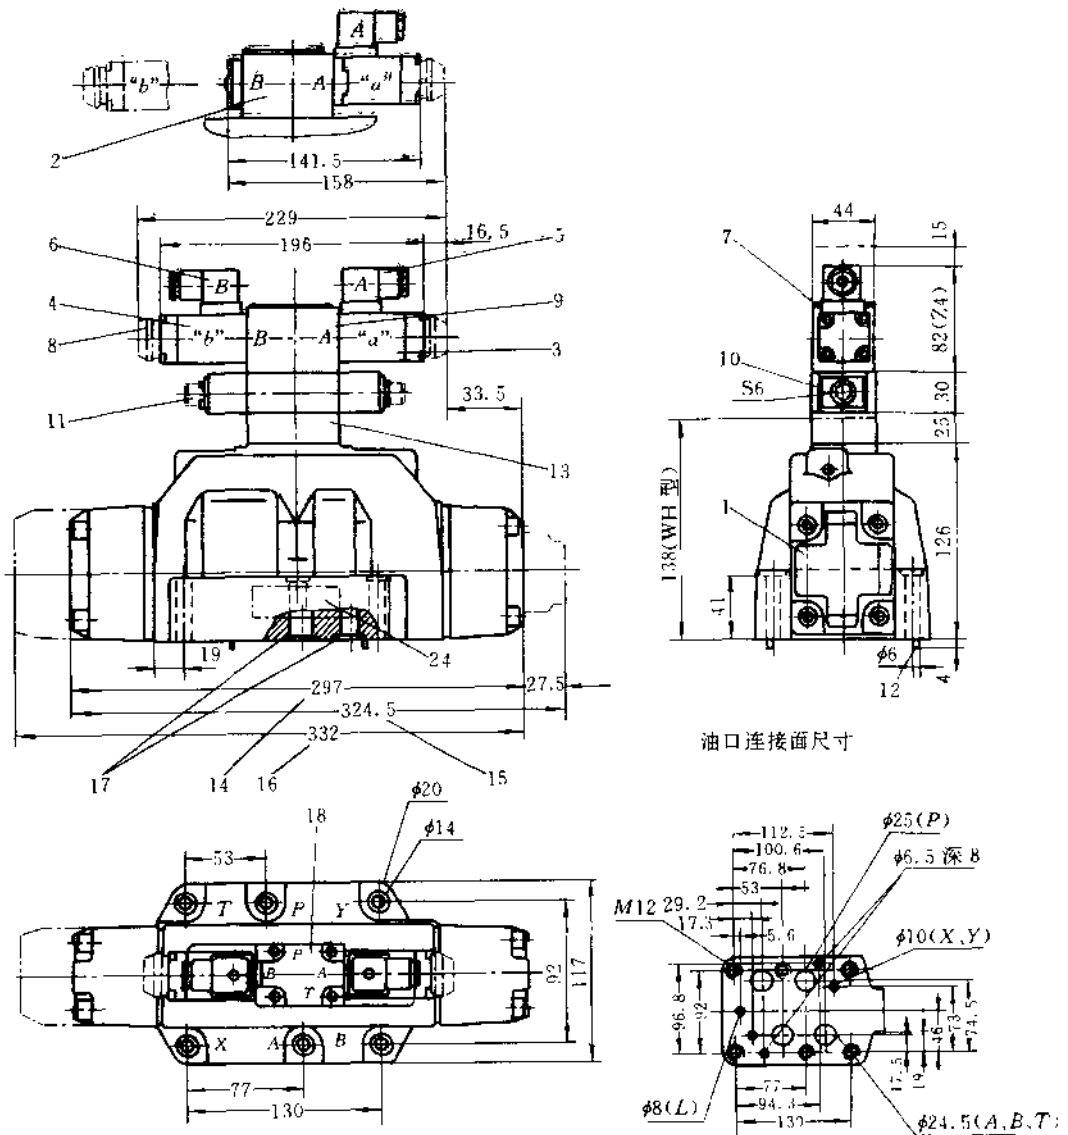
WEH/WH25 型换向阀外形连接尺寸图
